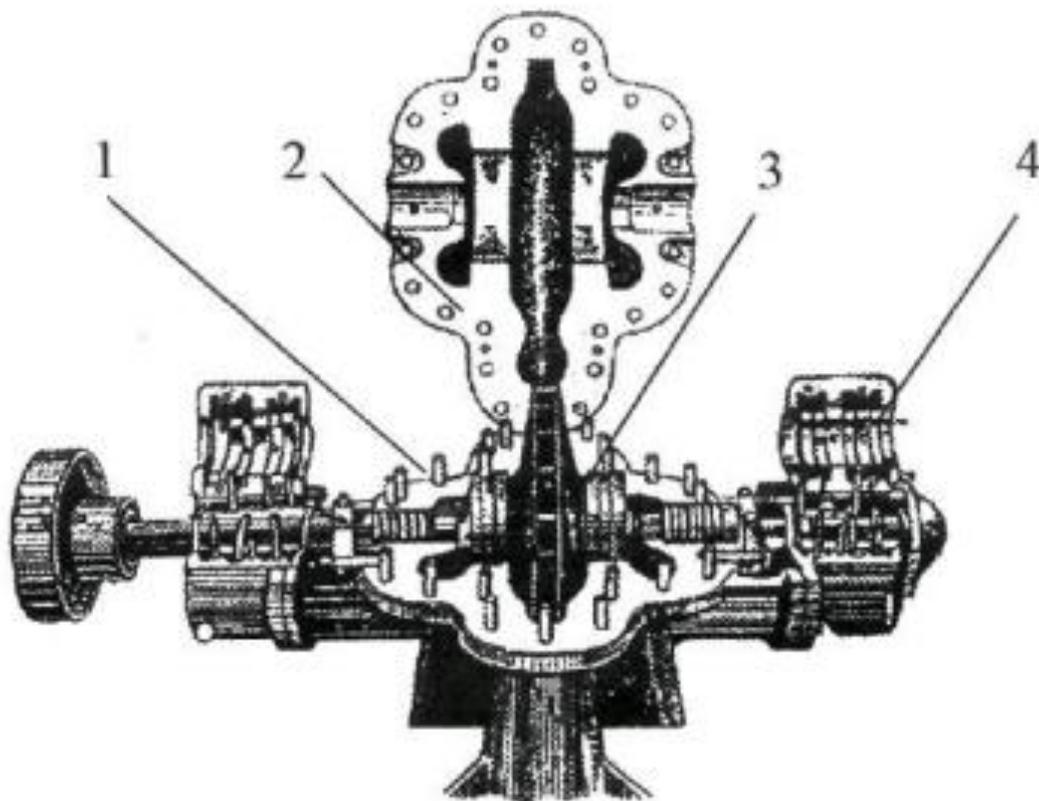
Насос с откинутой верхней половиной корпуса: 1 – корпус; 2 – крышка корпуса; 3 – ротор насоса; 4 – крышка подшипника
